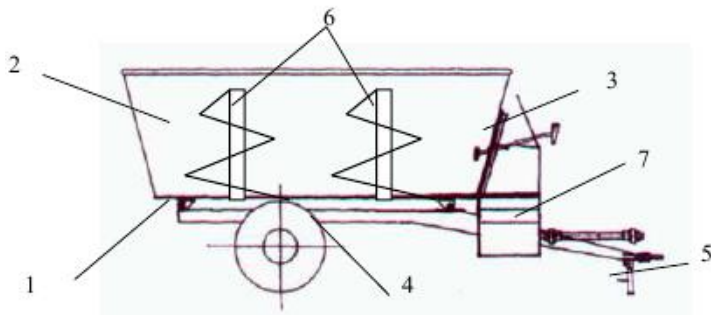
Конструктивна схема кормороздавача Solomix 2: 1 – рама, 2 – бункер, 3 – дозуючий клапан, 4 - балка з колесами, 5 – стоянкова опора, 6 – шнек, 7 – вивантажувальний транспортер.
